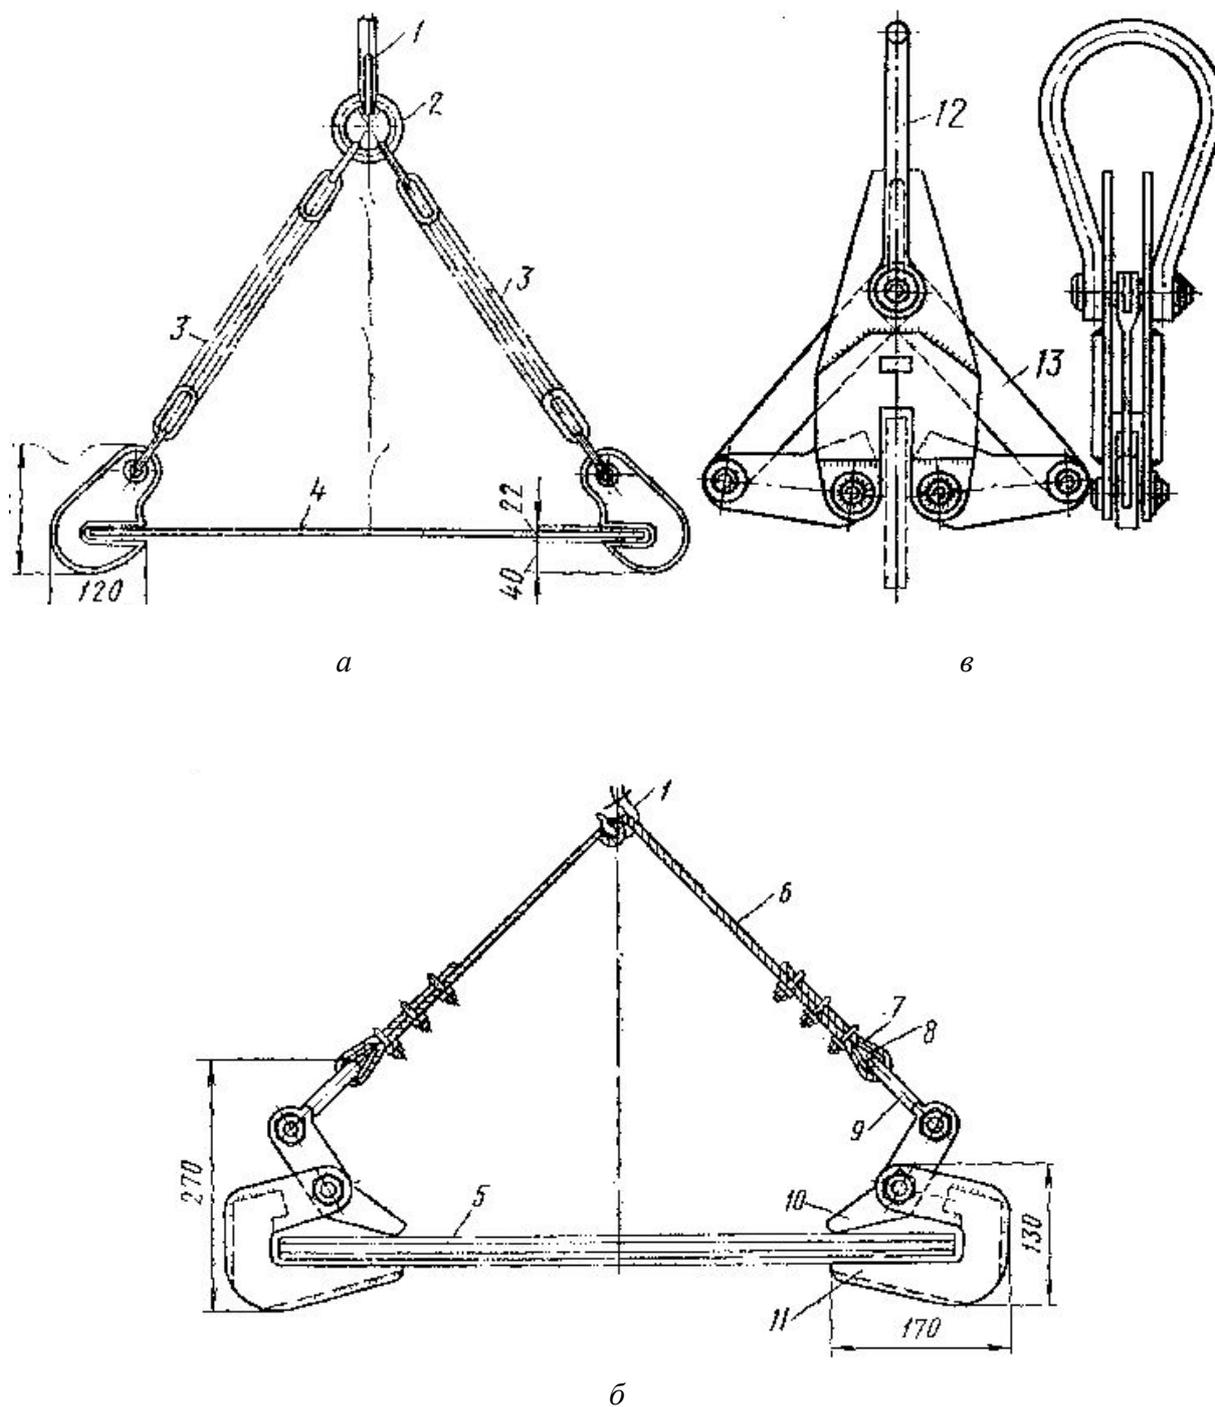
Схемы строповки захватами: *а* – захват для подъема одного листа, *б* – пакета листового металла, *в* – вертикальных листов: 1 – крюк грузоподъемного механизма; 2 – кольцо; 3 – цепной строп; 4 – поднимаемый лист металла; 5 – пакет металла; 6 – канат; 7 – петля; 8 – коуш; 9,11 – скобы; 10 – рычаг; 12 – серьга; 13 – рычажно-эксцентриковая система
